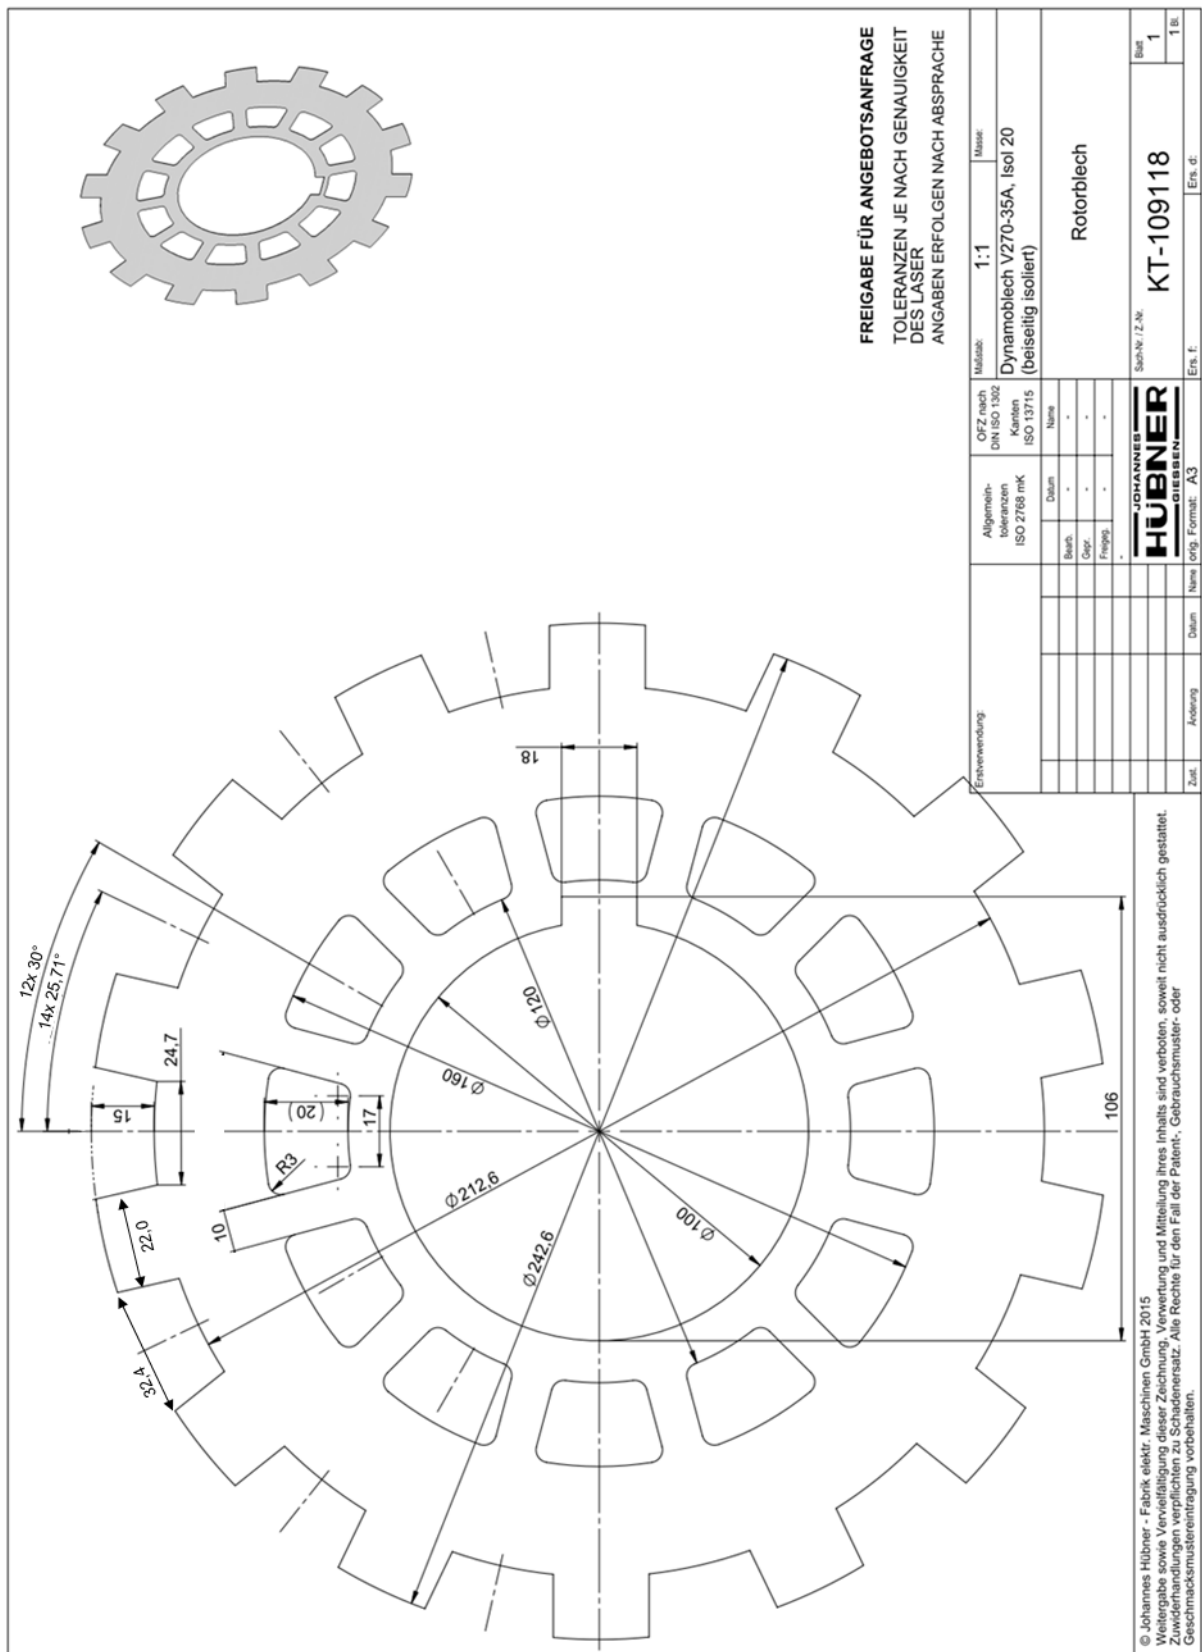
Technische Zeichnung des Rotorblechs der Prototyp-FSM
